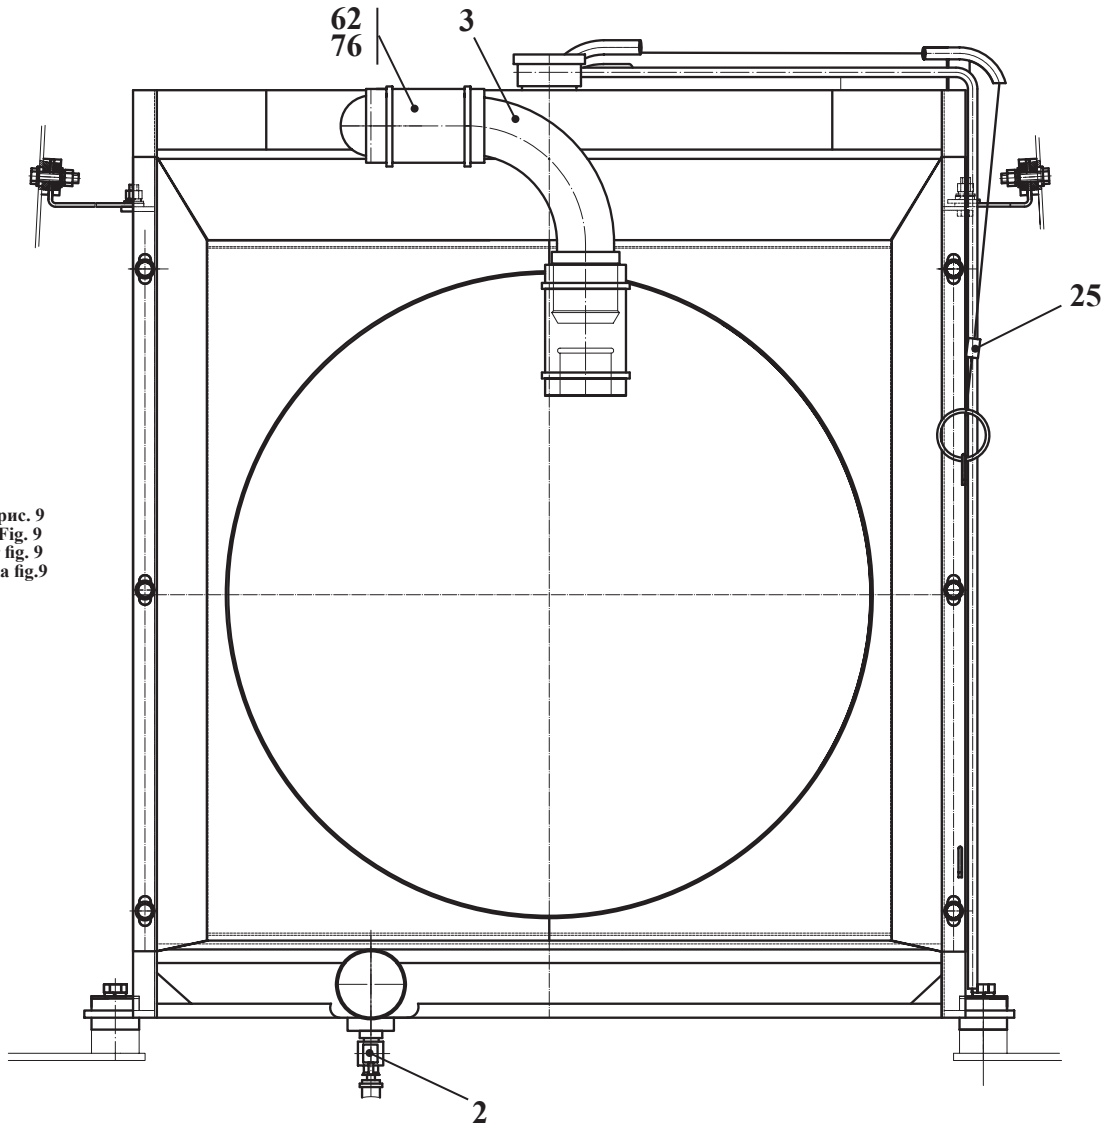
ТО-28А.02.18.000	Установка радиаторов
